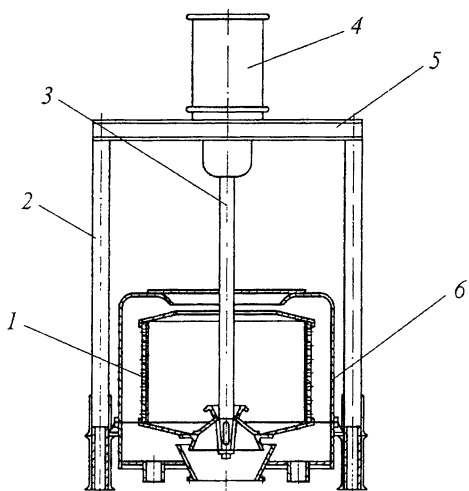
Конструктивная схема центрифуг типа ФПН, ОПН и ФПД:
